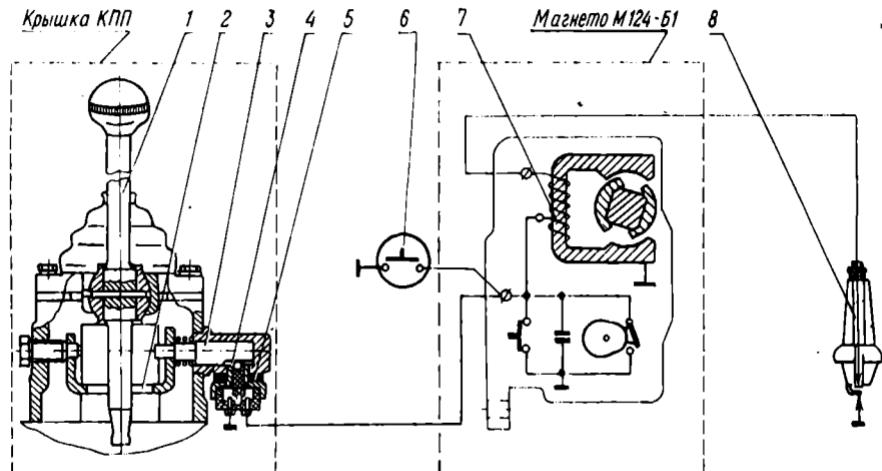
Схема блокировки запуска дизеля Д-240Л:
